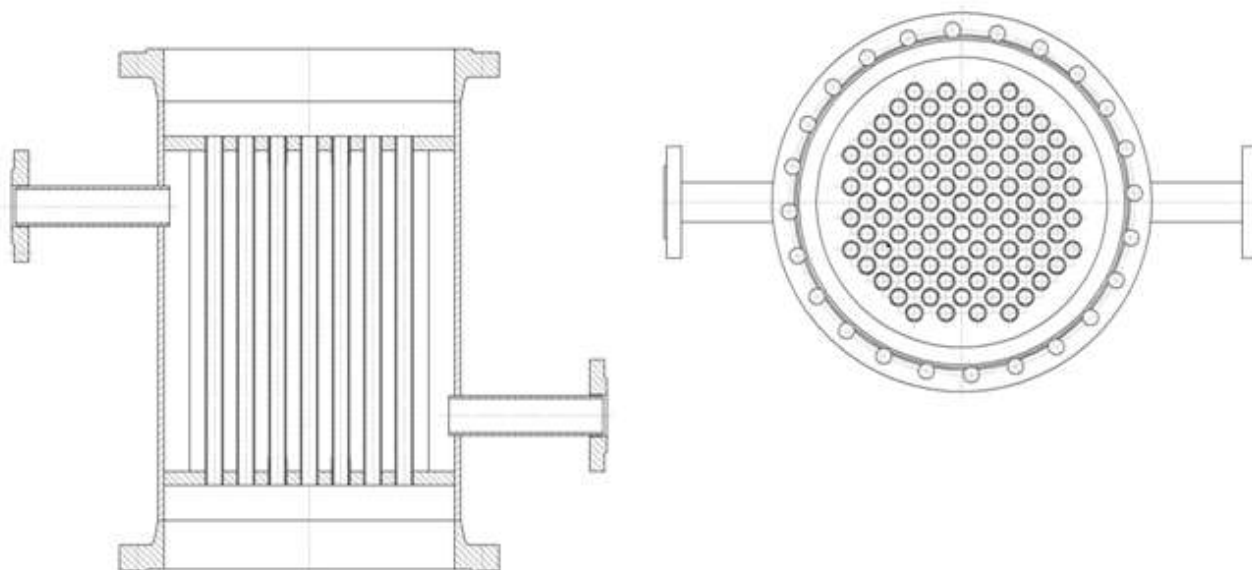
Схема кожухотрубного випарника етанової колони
